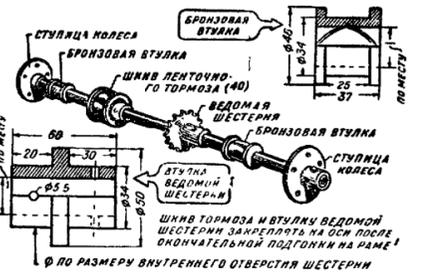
Задняя ось с деталями. В таком виде задняя ось устанавливается на раму. Сверлить в оси отверстия для болтов, крепящих шкив тормоза и втулку ведомой шестерни, следует после окончательной подгонки и регулировки тормозной тяги и моторной цепи на раме.
